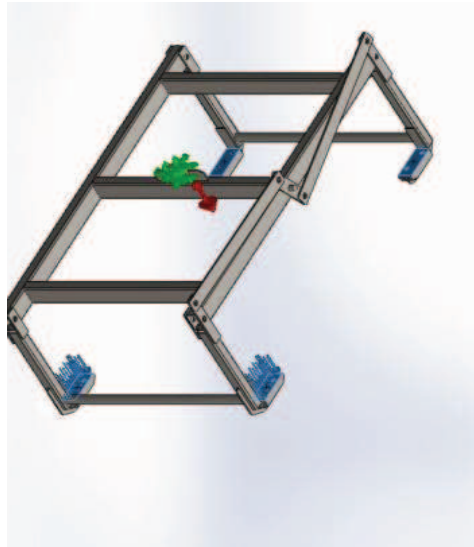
18 Cargas y Restricciones en el Dispositivo de Elevación del Carrocería Final
